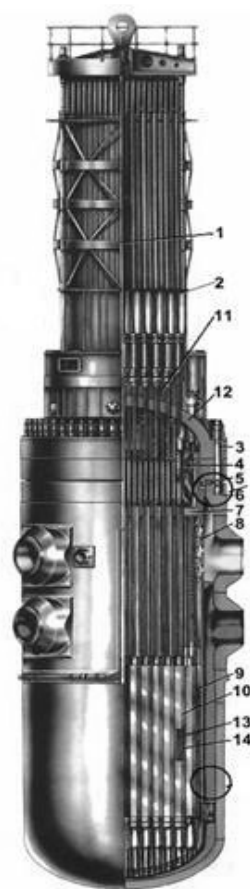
Реактор ВВЭР-1000 в сборе: 1 – верхний блок; 2 – привод СУЗ; 3 – шпилька; 4 – труба для загрузки образцов-свидетелей; 5 – уплотнение; 6 – корпус реактора; 7 – блок защитных труб; 8 – шахта; 10 – топливные сборки; 11 – теплоизоляция реактора; 12 – крышка реактора; 13 – регулирующие стержни; 14 – топливные стержни
